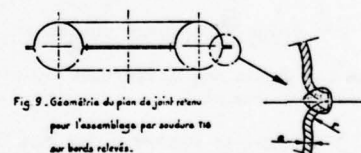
Géométrie du plan de joint relevé pour l'assemblage par soudure TIG aux bords relevés.
